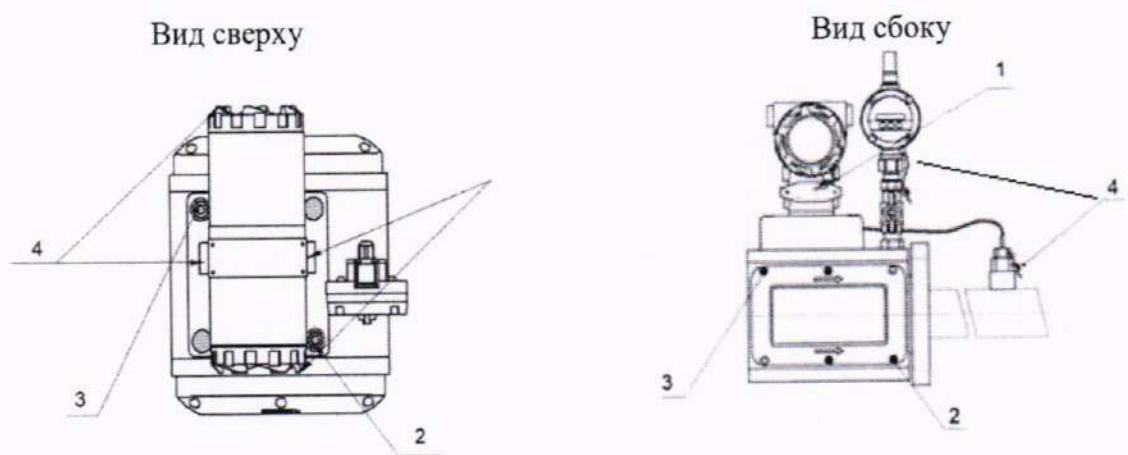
Корпус прямоугольного сечения с совмещенными защитными крышками
